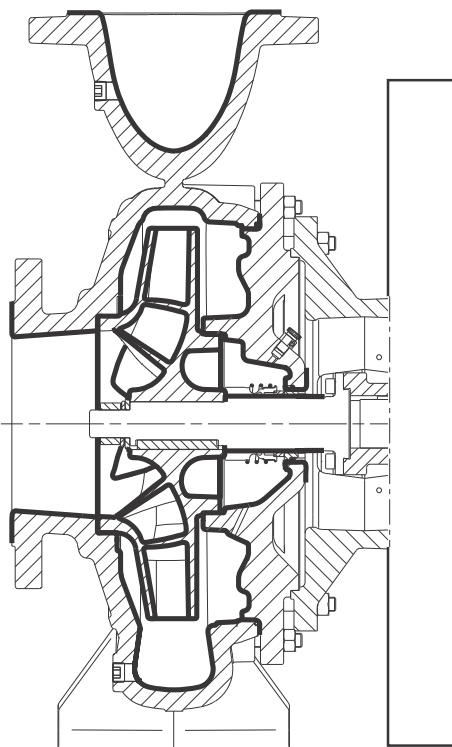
Schnittzeichnung von Pumpen mit Beschichtung für Seewasser von 25 bis 65 °C
